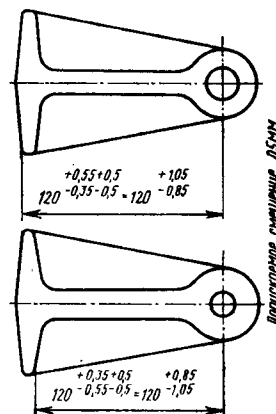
Пример назначения допусков на размер между осевой линией и необрабатываемой поверхностью, когда штамповка производится в двух половинках штампа.
